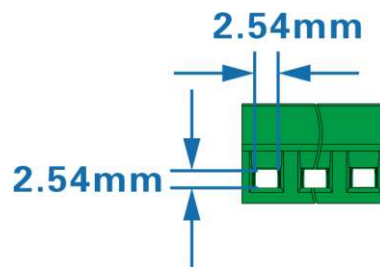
borne de câble RS485 (plage de section transversale du conducteur 0,25-1 mm^2)
